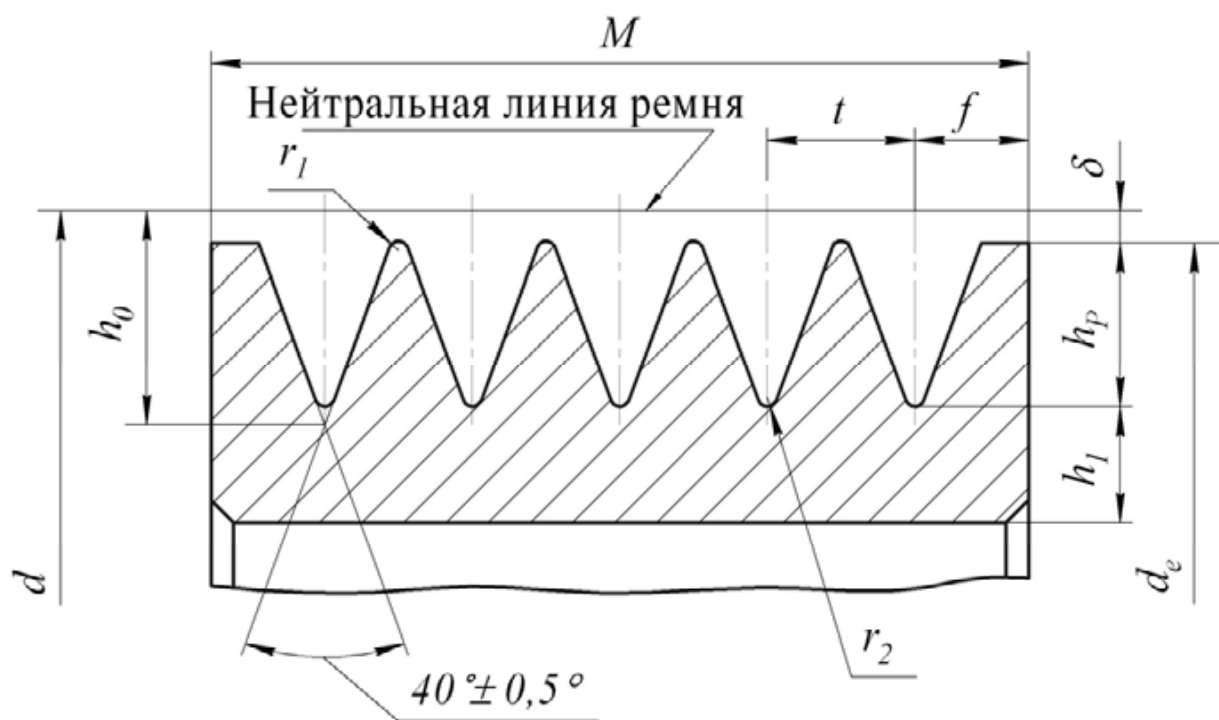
Профиль канавок шкивов для поликлиновых ремней
